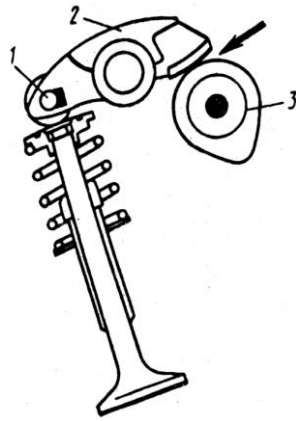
Привод клапанов через коромысло и регулировочный эксцентрик:
